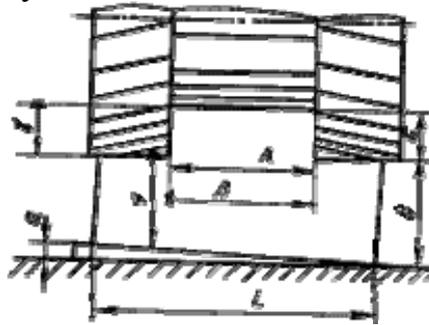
Обработка заготовки с соблюдением принципа единства баз
